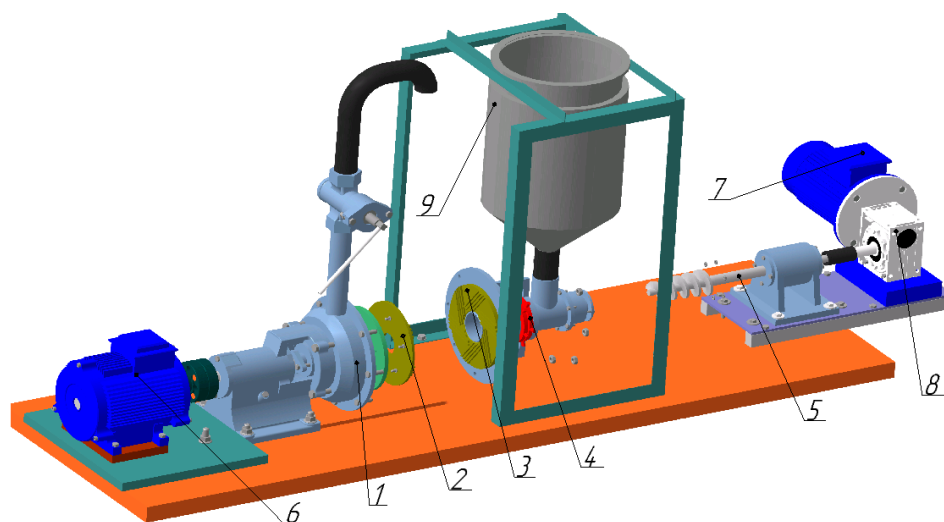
Схема размольной установки (1 - зона размола; 2 - ротор; 3 - статор; 4 – присадочное устройство; 5 – шнековый питатель; 6 – электродвигатель ротора; 7 – электродвигатель привода шнекового питателя; 8 – червячный редуктор привода шнекового питателя, 9 – емкость для волокнистой массы)
